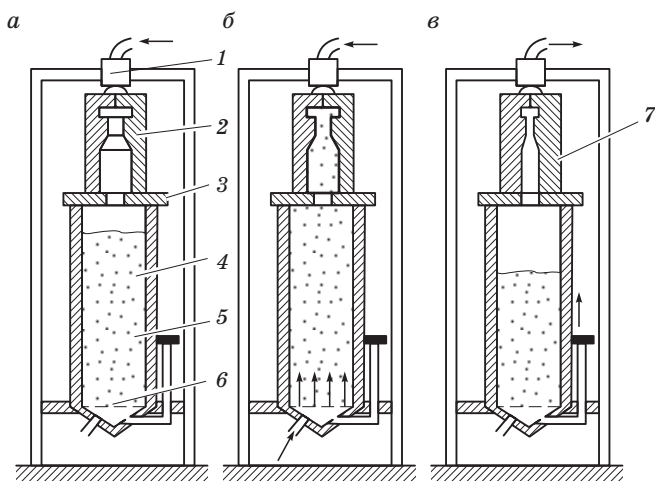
Схема пескоудного изготовления оболочкового стержня
